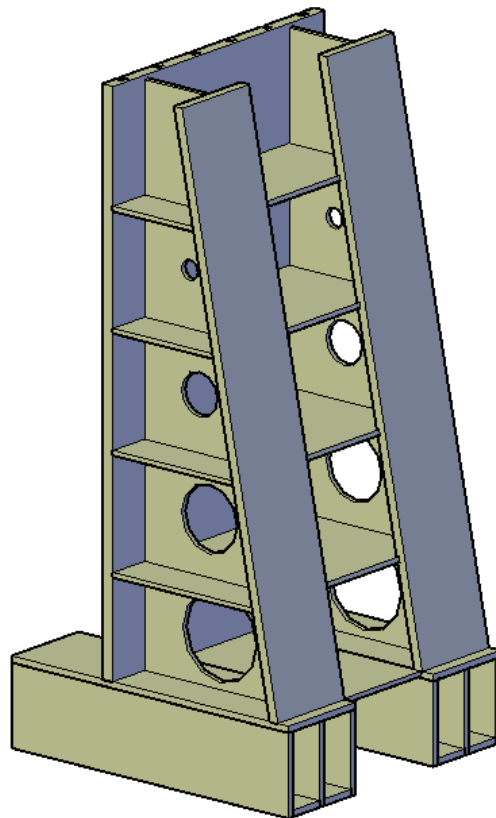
Assemblaggio elemento strutturale di tipo piastra con scanalature a "T"
